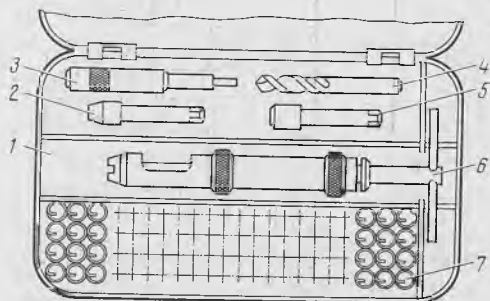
Комплект приспособлений для ремонта резьбовых отверстий спиральными вставками:
